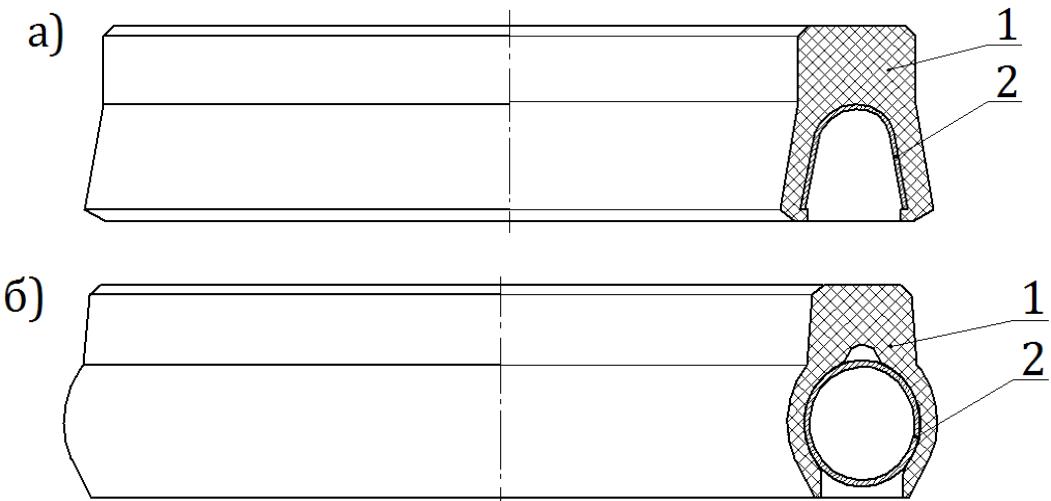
Внешний вид манжеты: а – с пластинчатой пружиной,
